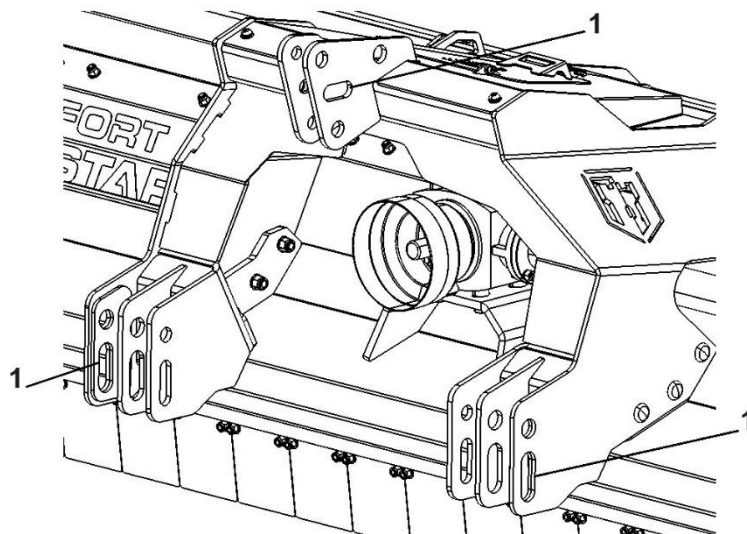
Schwimmstellung der Maschine: 1 – Bohrungen in der Aufhängung des Dreipunkt-Krafthebers (TUZ), die für den Betrieb der Maschine in Schwimmstellung vorgesehen sind
